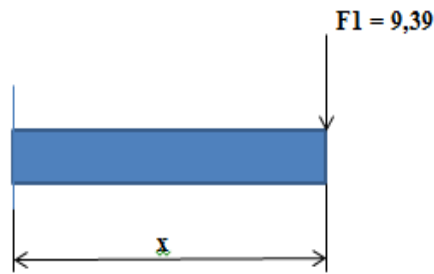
Fuerzas que actúan sobre la placa que soporta el motor de arranque
